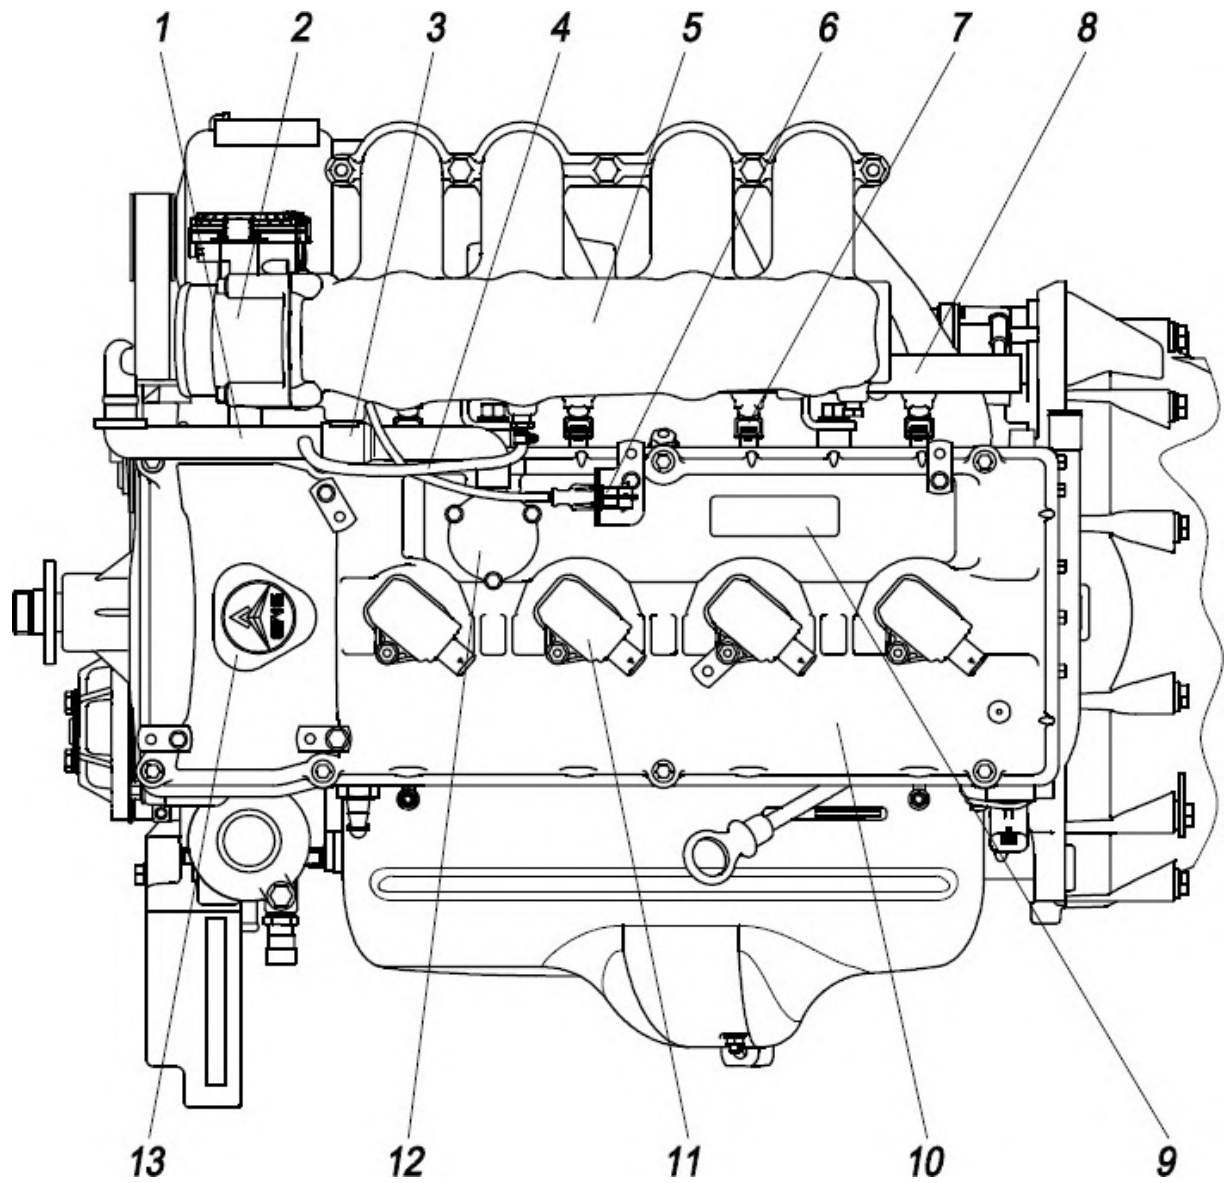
Draufsicht auf den Motor ZMZ-40904.10:
